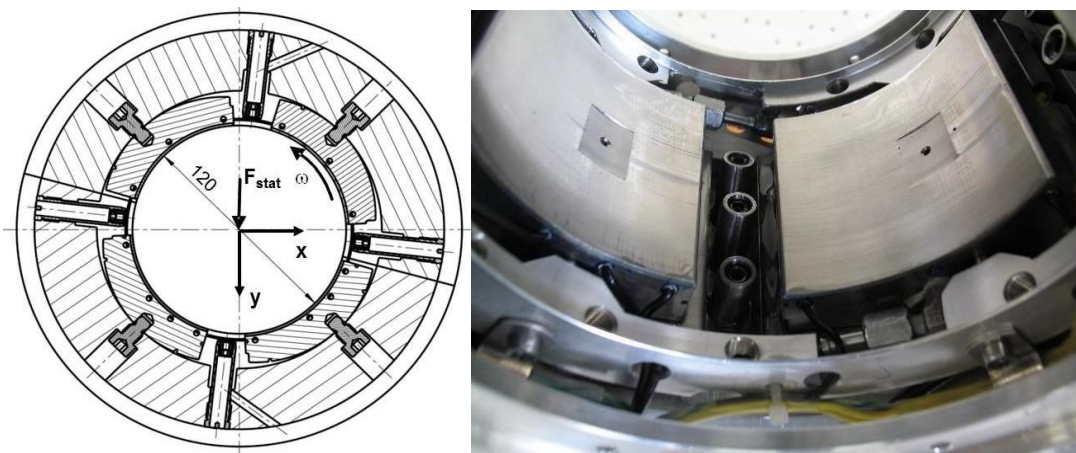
Конструкція підшипника ковзання з поворотними сегментами [18]
